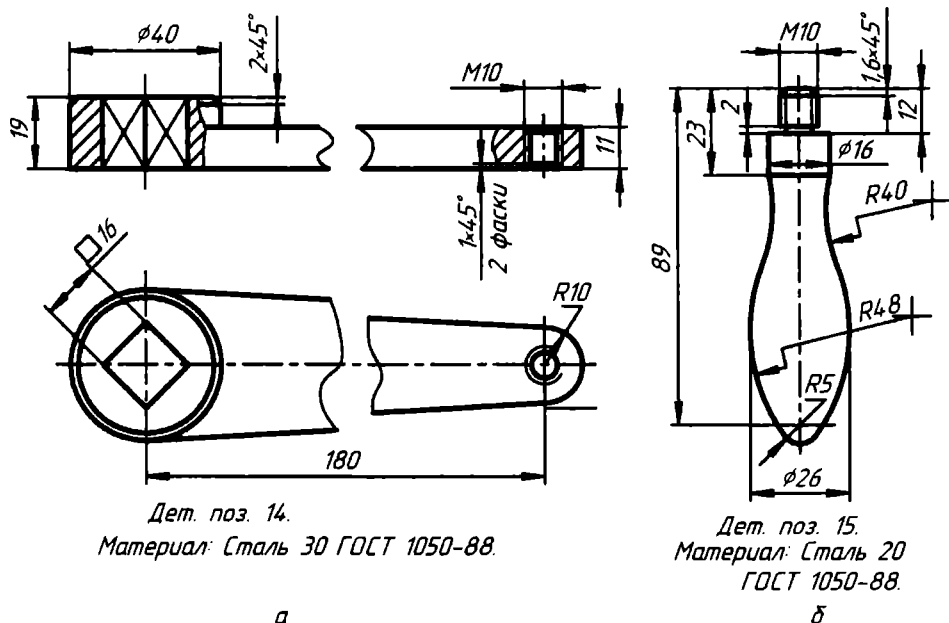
Чертежи: а — рукоятки; б — ручки
